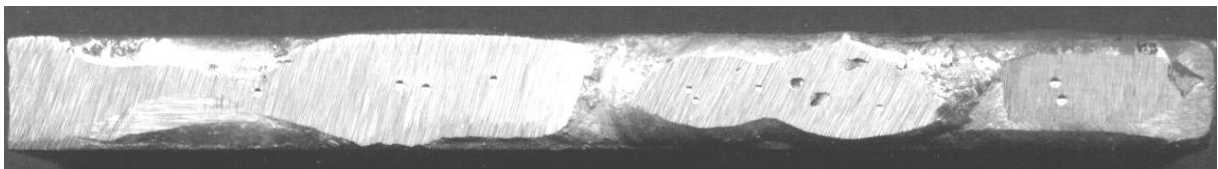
Поверхность образца, наплавленного порошком ПР-НХ16СР3 методом плазменной наплавки
